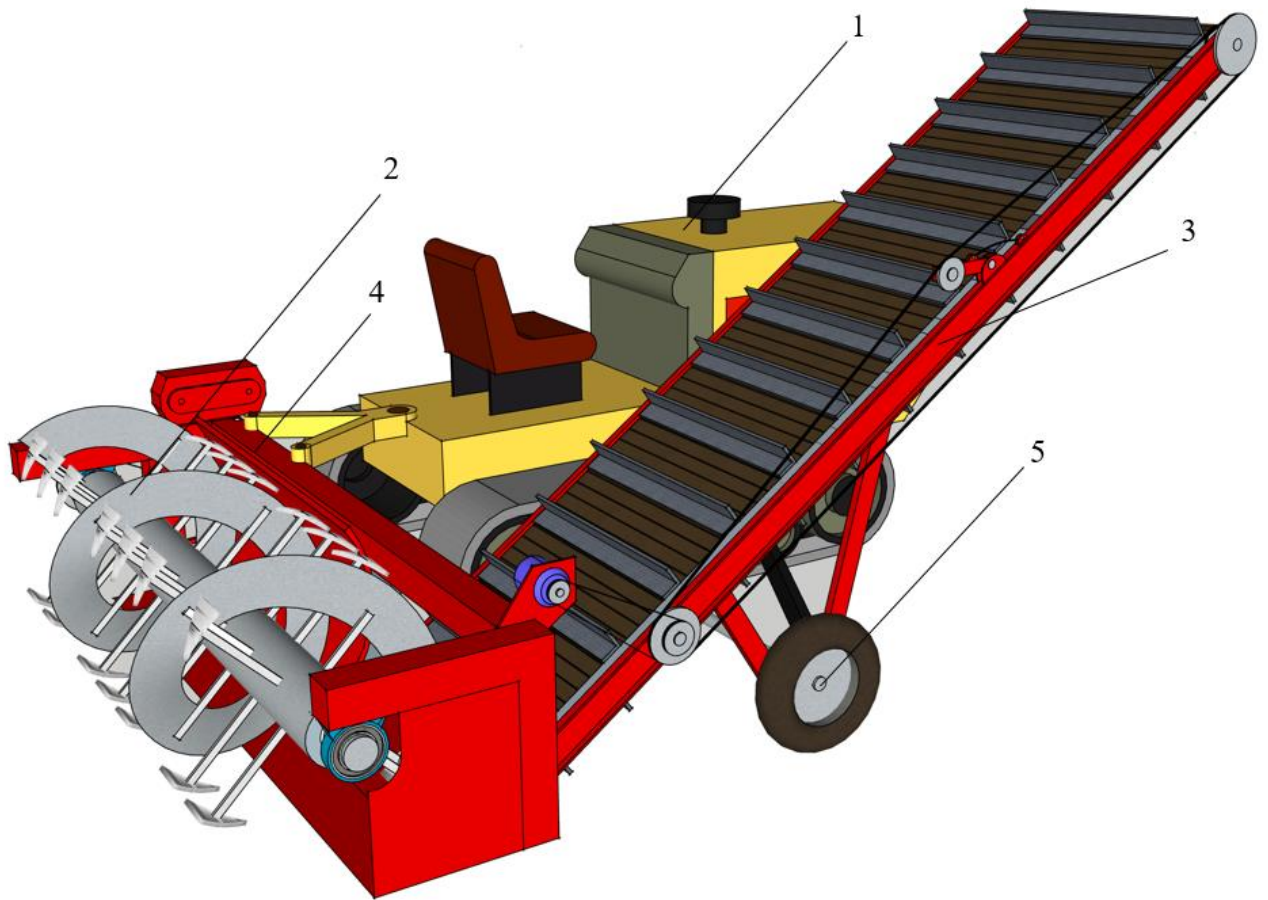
Схема погрузчика-смесителя: 1 – базовый трактор; 2 – рабочий орган в виде ленточного шнека с установленными на стойках зубьями; 3 – отгрузочный ленточно-планчатый транспортер; 4 – общая рама погрузчика; 5 – опорное колесо
